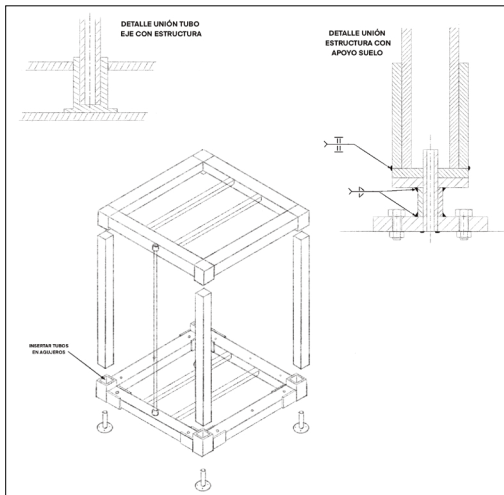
Estructura interior del stand y detalles de soldadura.
